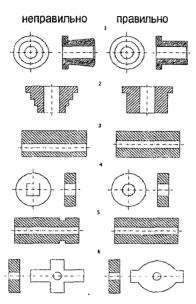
Примеры конструирования металлокерамических заготовок
